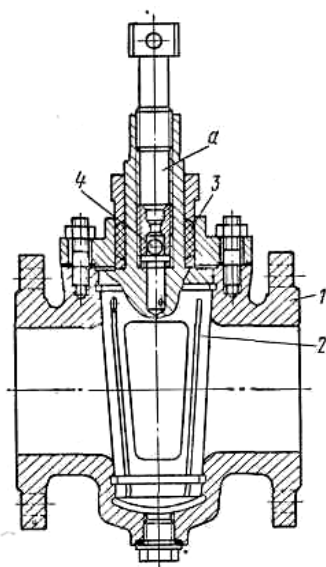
Сальниковый кран со смазкой: 1 – корпус; 2 – пробка; 3 – набивка сальника; 4 – обратный шариковый клапан; а – камера для смазки
